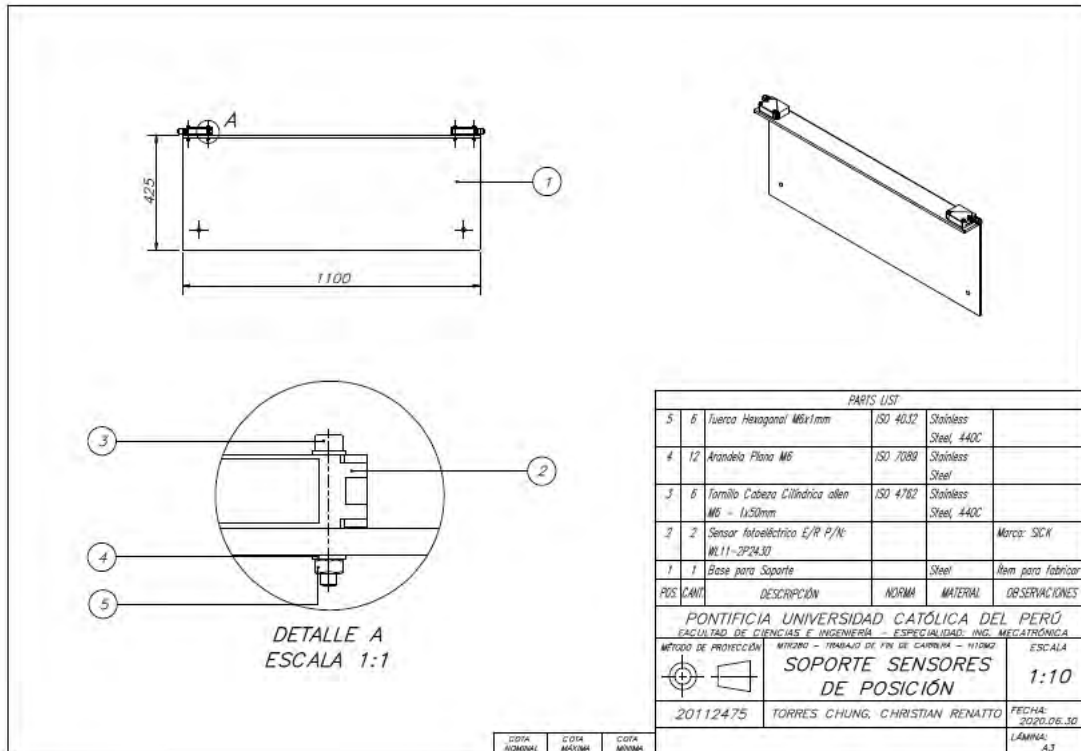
Estructura de sensores de posicionamiento. Plano. Fuente: Propia.
